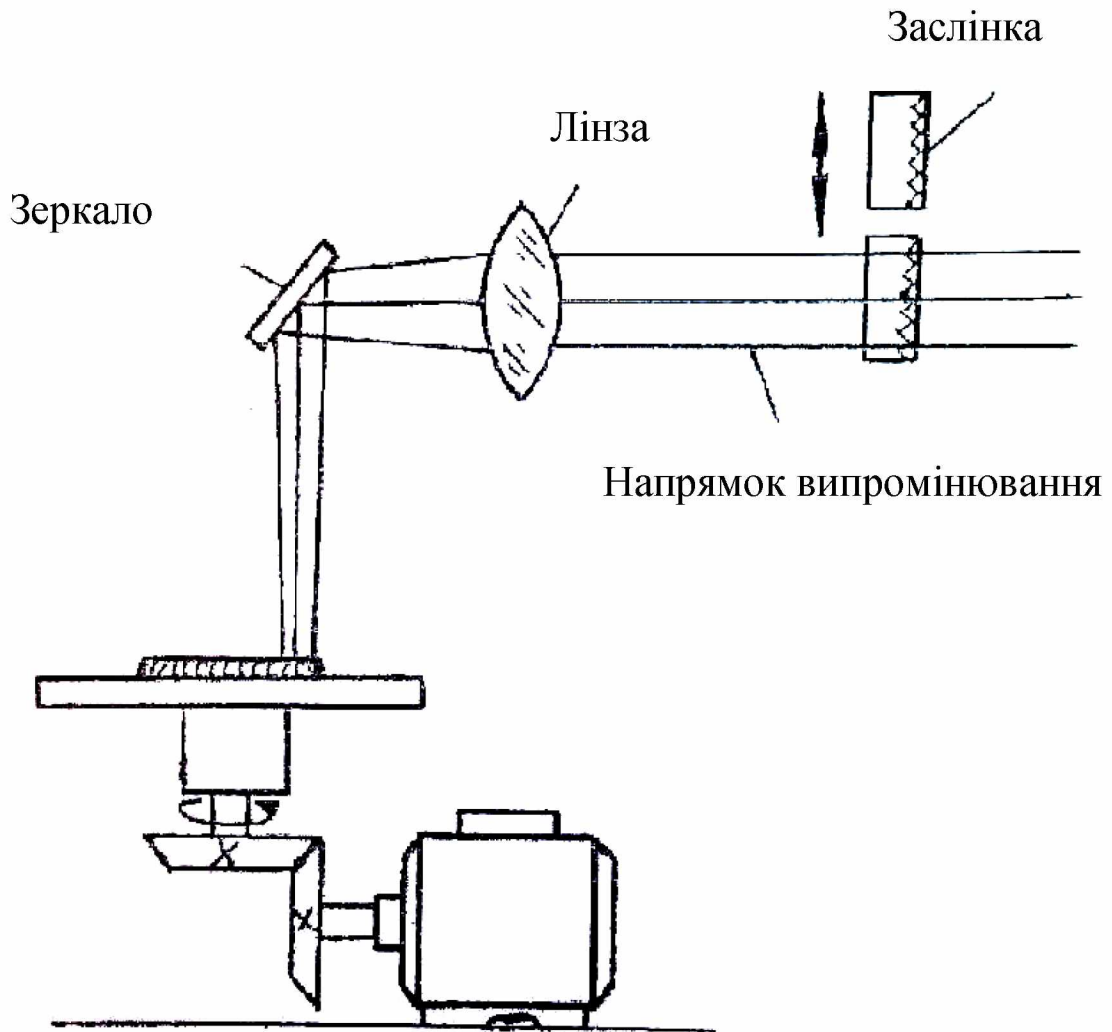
Схема лазерного наплавлення одиничного колового валика
